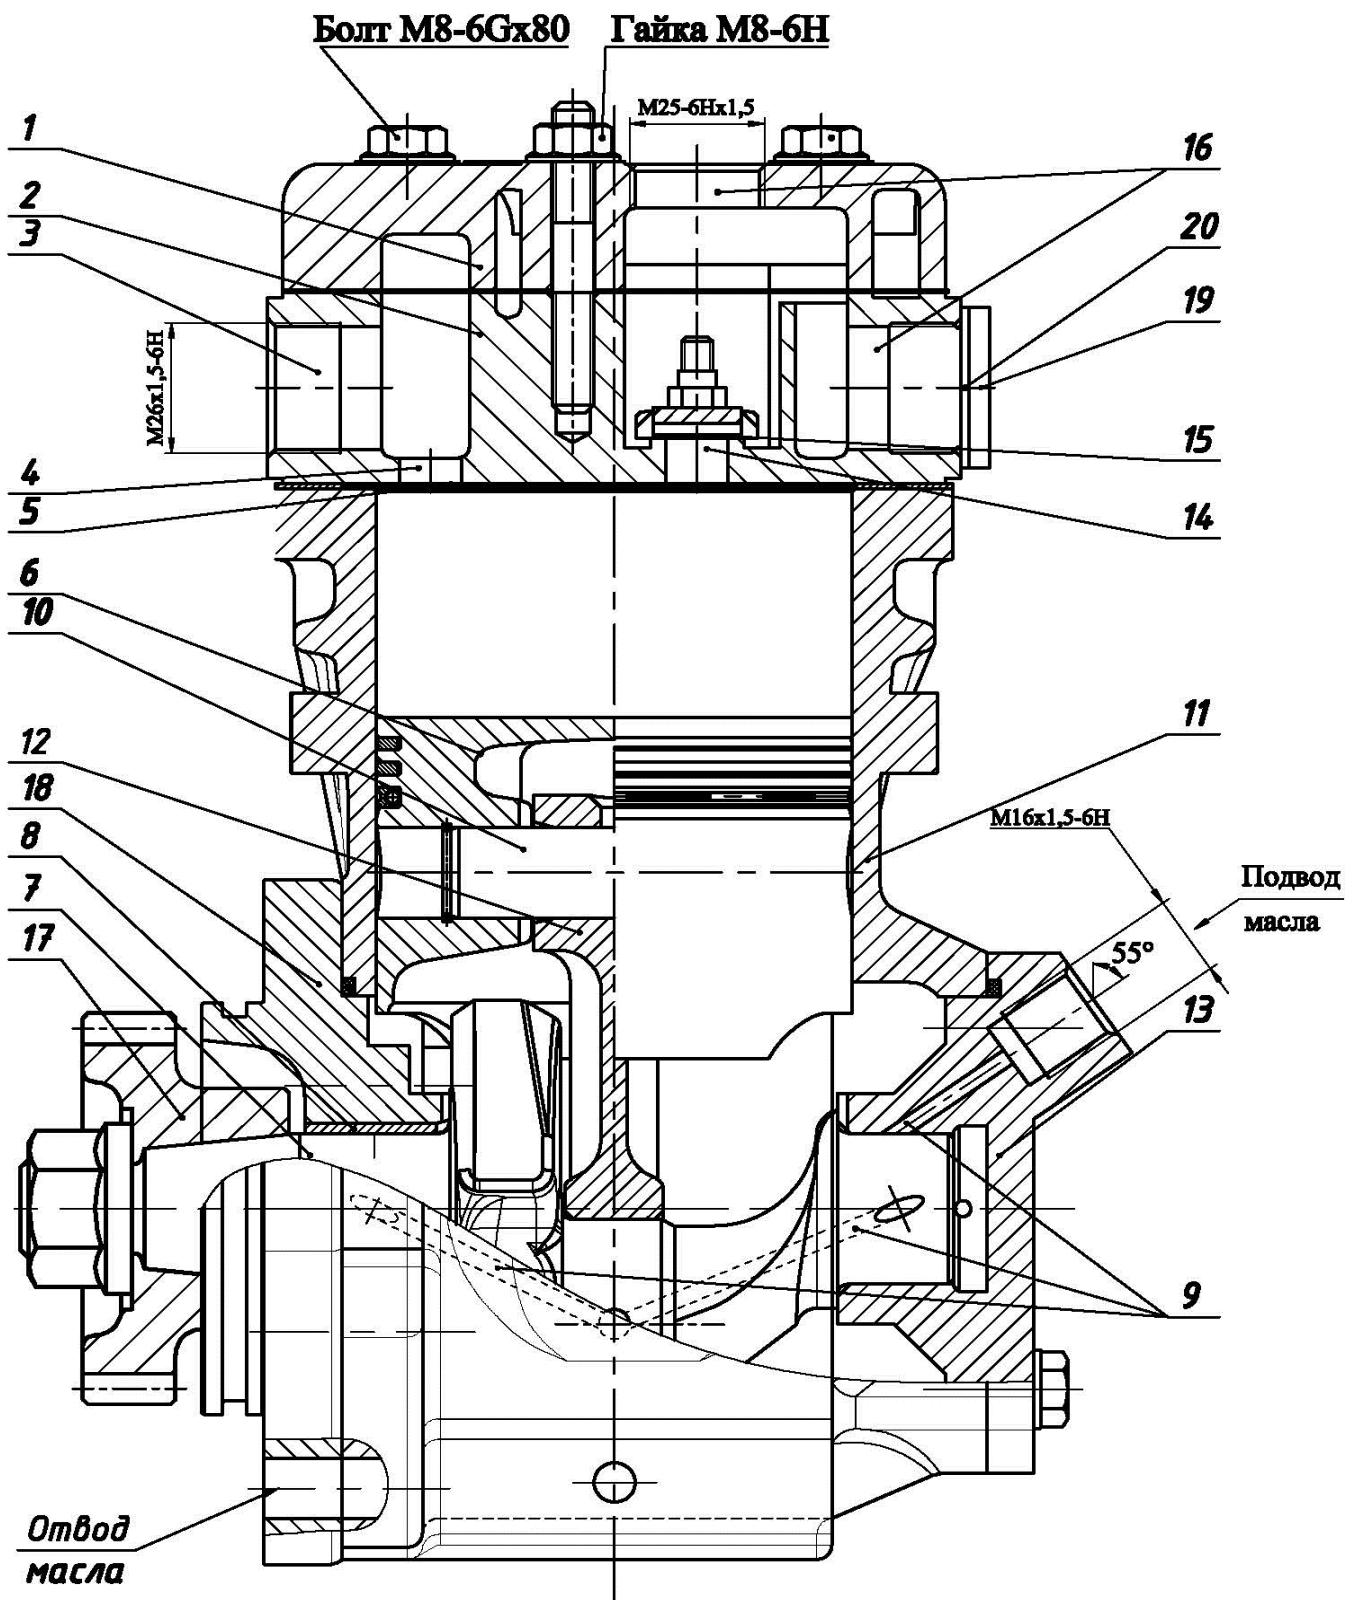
Принципиальная схема компрессоров АМ.3509015-11:
